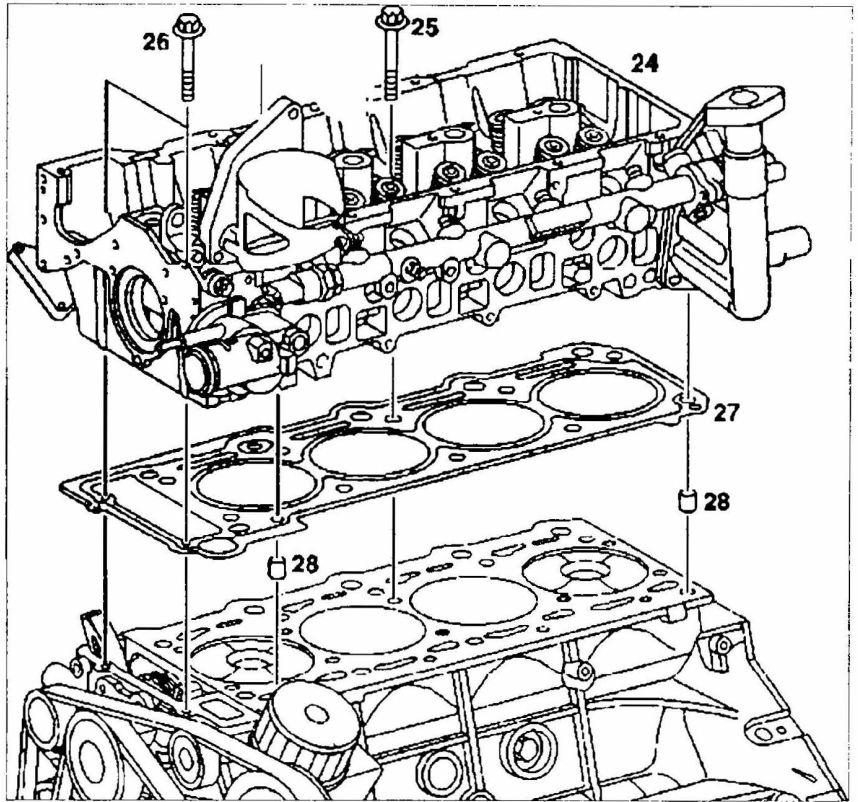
Снятие и установка головки блока цилиндров (показано на двигателях 611):
